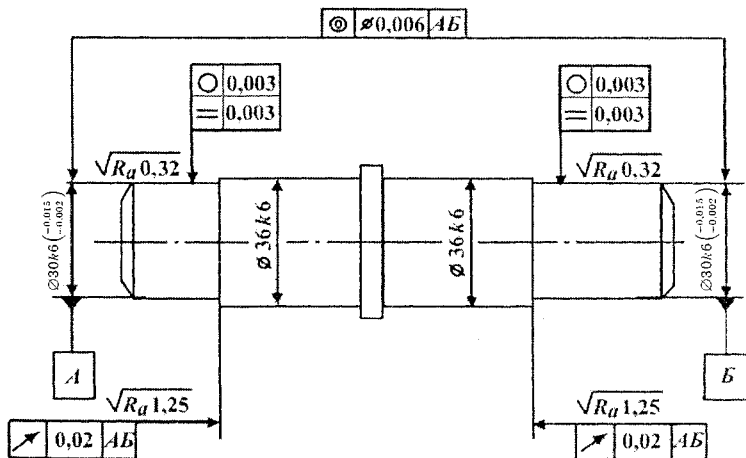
Пример обозначения точностных требований к поверхностям вала, сопрягаемых с подшипником качения
